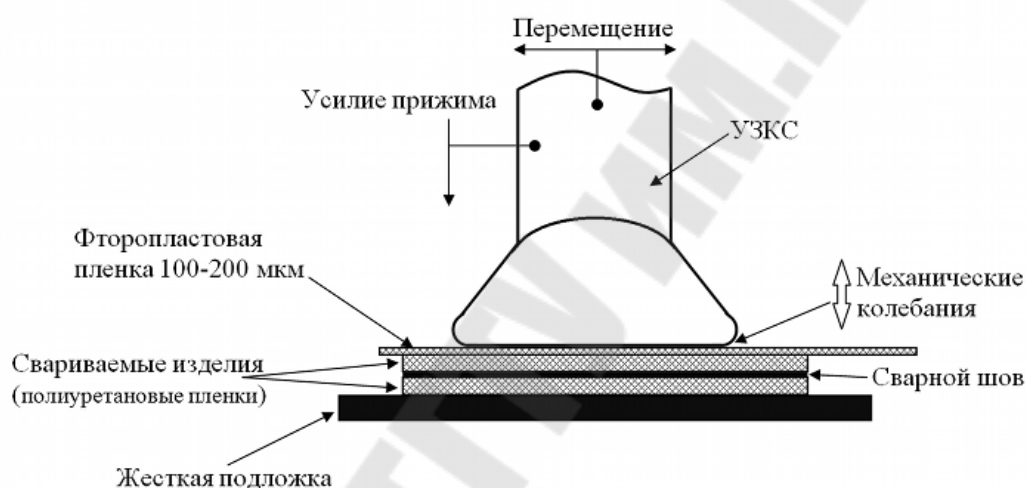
Схема проведения ультразвуковой сварки полимерных пленок
